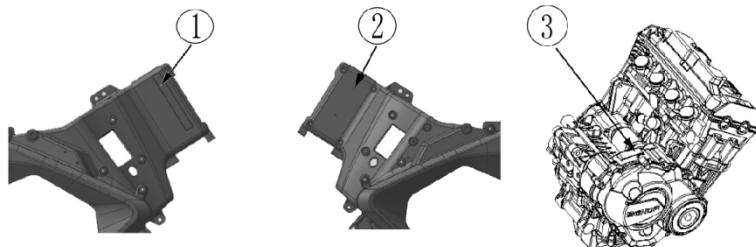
Схема расположения заводской таблички, номера рамы, VIN-кода и номера двигателя
